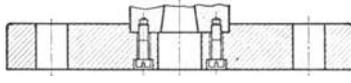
Befestigung der Schnittplatte durch Zugschrauben und Einsenkung.
